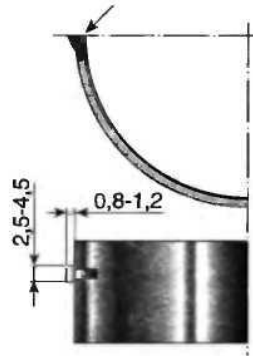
Класична конструкція замкового механізму підшипника ковзання.
